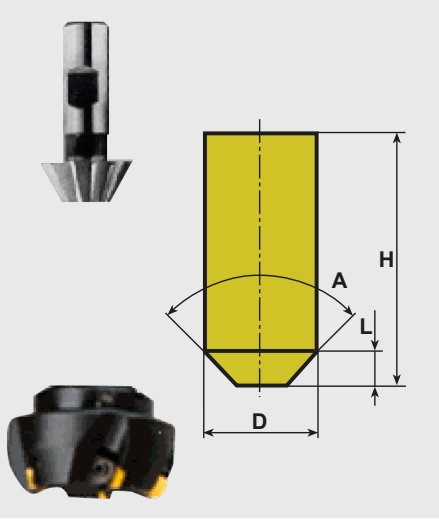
Werkzeugbeschreibung TOOL/CHAMFER Fräser mit Fase
